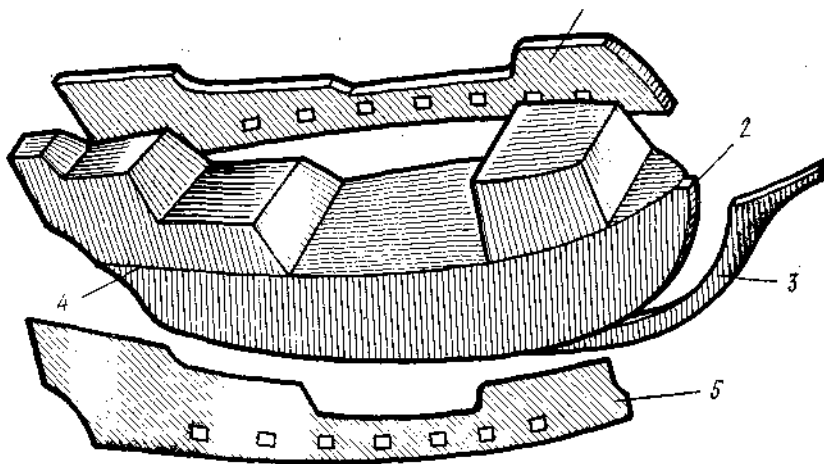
Изготовление корпуса модели старинного парусного корабля:
